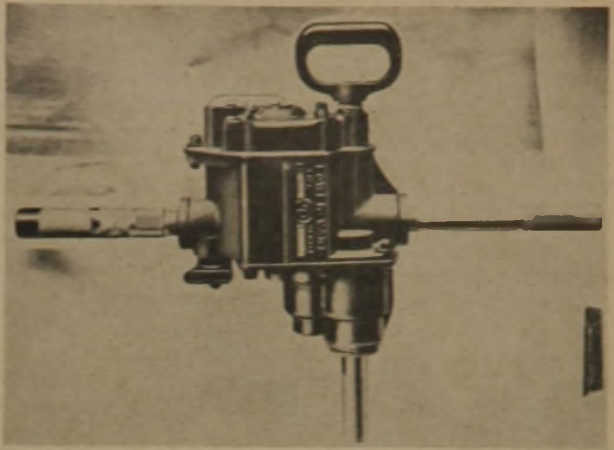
Elektronguß für Preßluftwerkzeuge (England)
